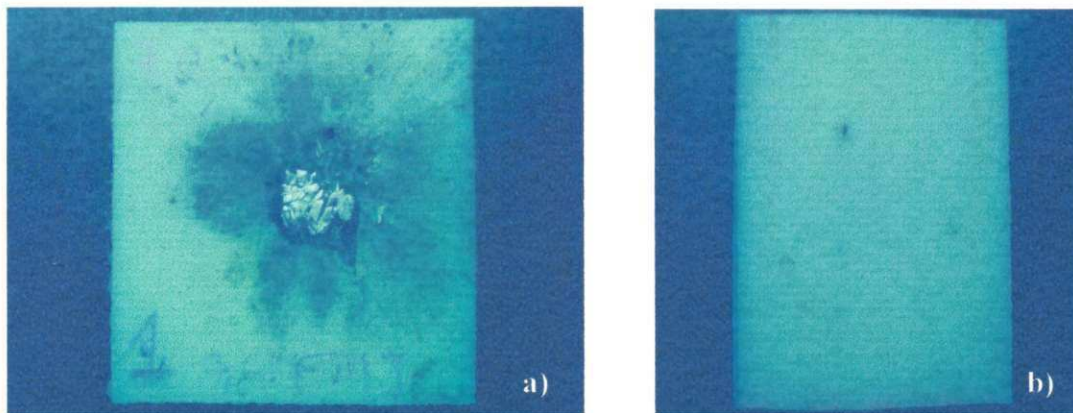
Placa de retaguarda de PEUAPM após o impacto com munição 7.62 mm FMJ : a) vista frontal e b) vista traseira
